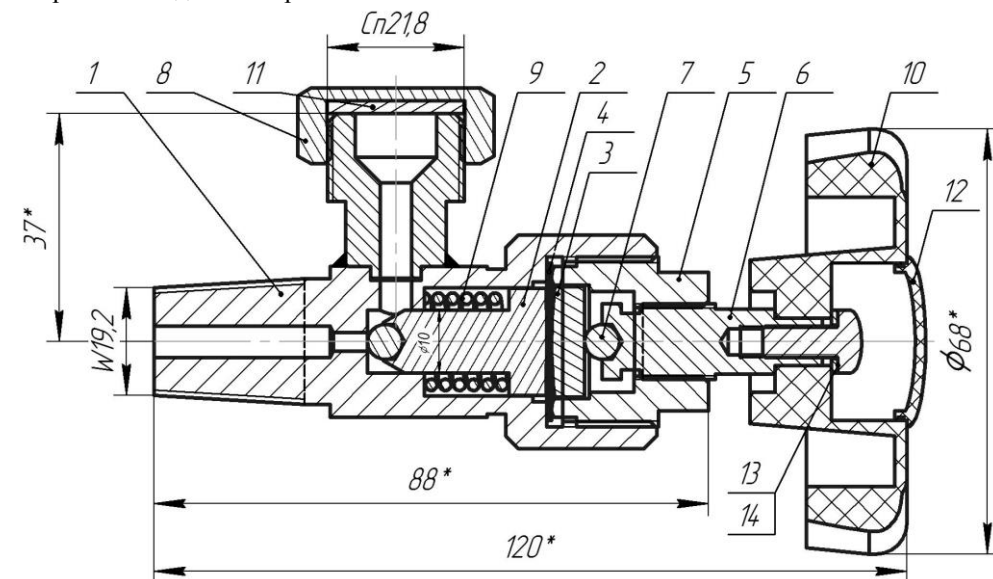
Вентиль ВС-16. 1 – Корпус; 2 – Золотник; 3 – Тарелка; 4 – Мембраны; 5 – Гайка; 6 – Шток; 7 – Шарик; 8 – Гайка; 9 – Пружина; 10 – Вороток; 11 – Прокладка; 12 – Крышка; 13 – Шайба М5; 14 – Винт с полукруглой головкой М5.
